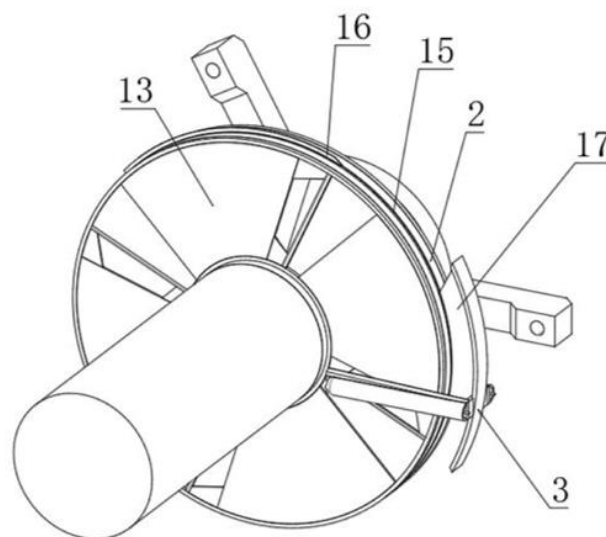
2. Фільтруючий сектор; 3. Вузол скребкового стрижня; 13. Зовнішня поверхня фільтра; 15. Канавка кільця; 16. Планка повітряної подушки; 17. Пресувальний блок.
